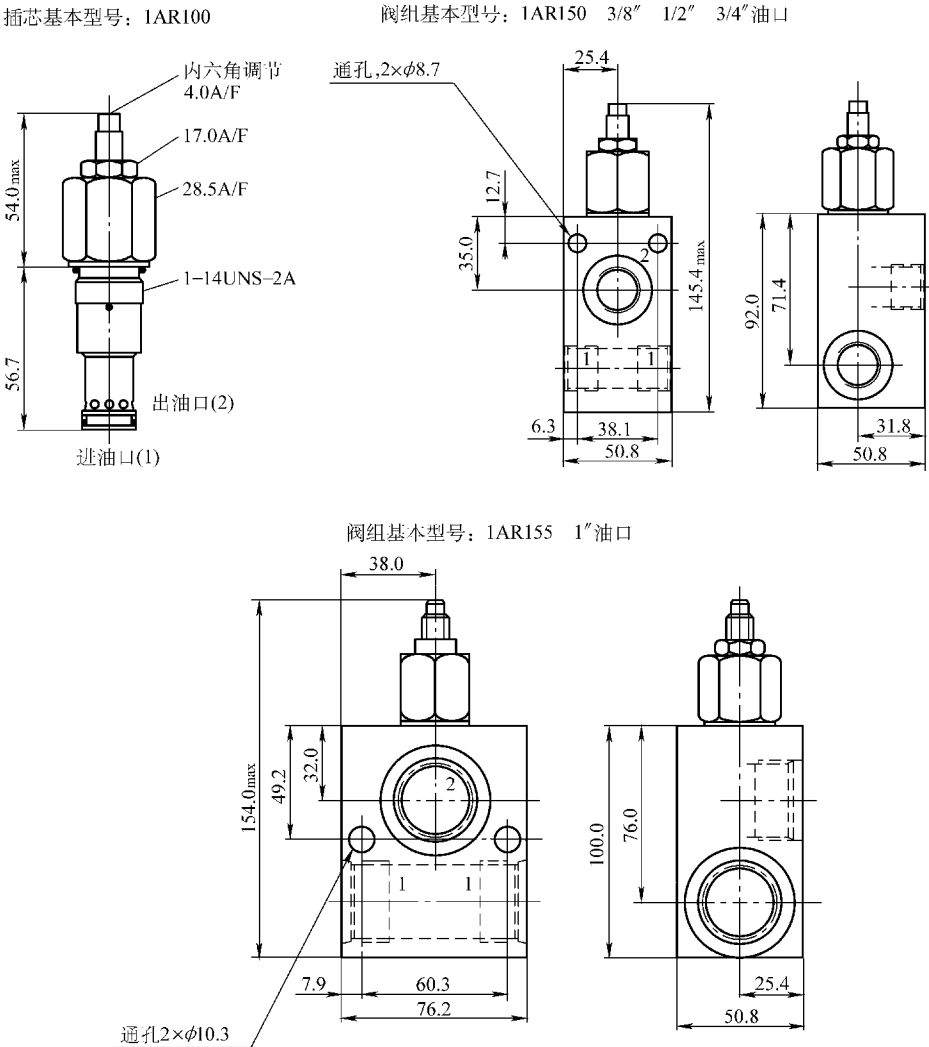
1AR100 型插芯及阀组外形尺寸
